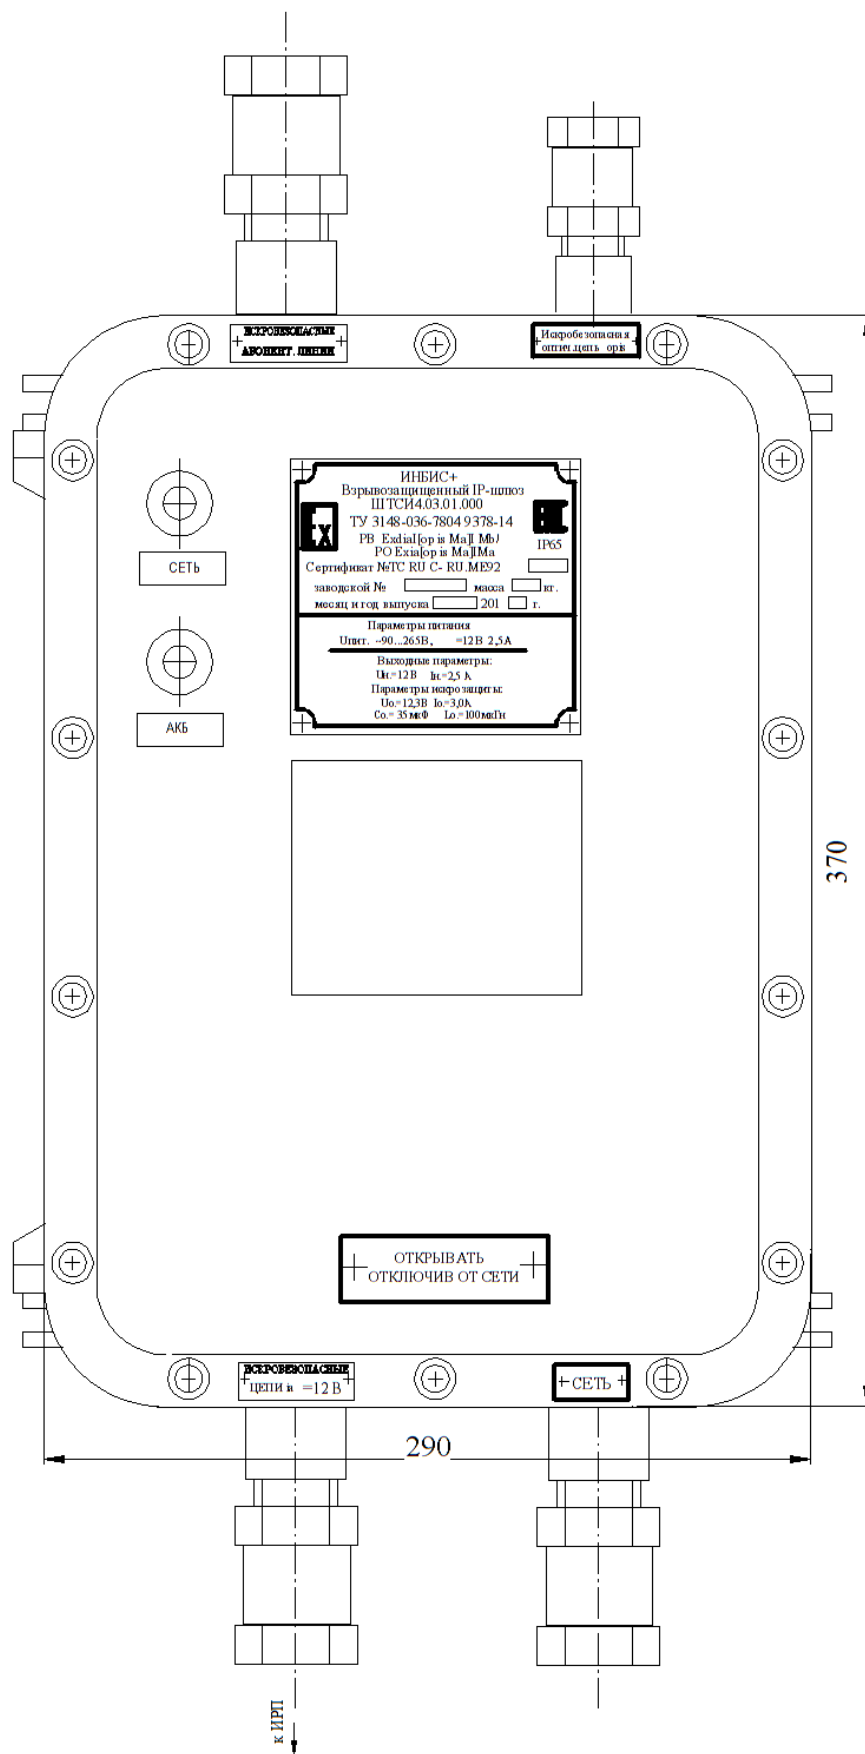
Чертёж корпуса IP- шлюза.
